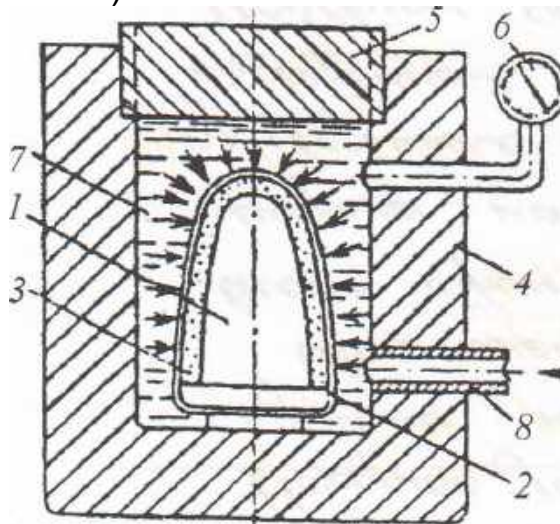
Схема гідростатичного пресування: 1 – стрижень; 2 – гумовий мішок; 3 – заготовка; 4 – корпус; 5 – кришка; 6 – манометр; 7 – рідина; 8 – мундштук
